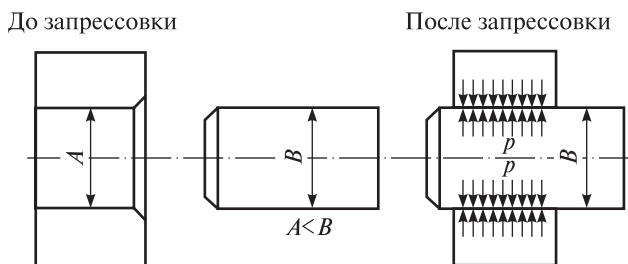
Изготовление натяга насаживанием одной детали на другую
